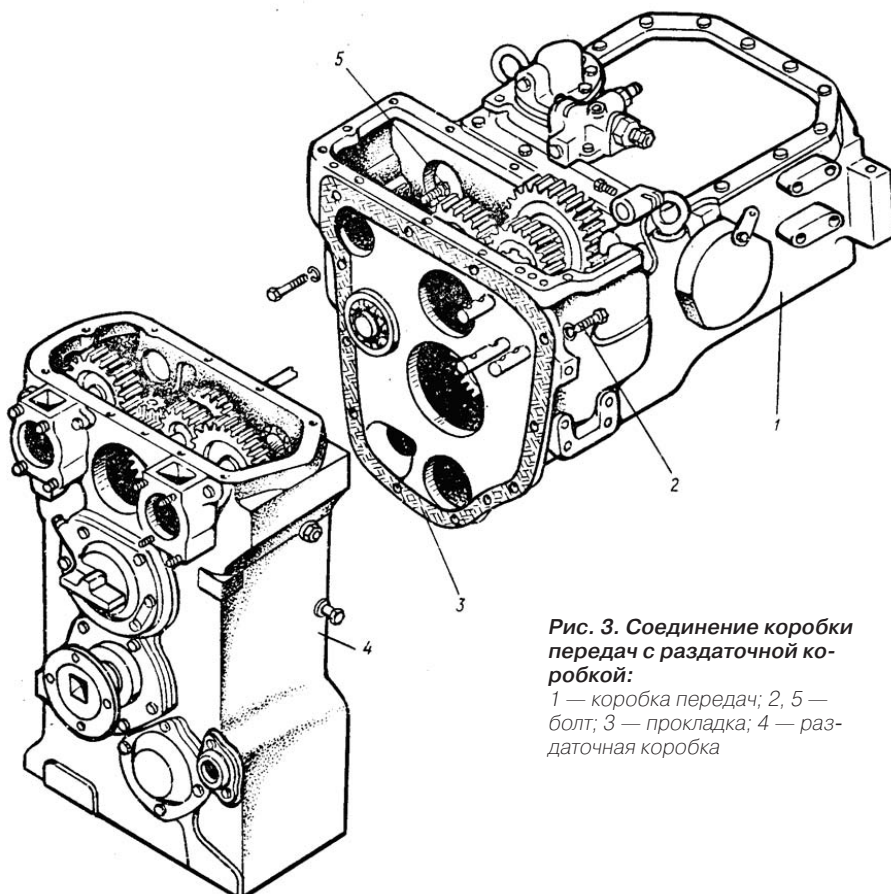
Соединение коробки передач с раздаточной коробкой: 1 — коробка передач; 2, 5 — болт; 3 — прокладка; 4 — раздаточная коробка
